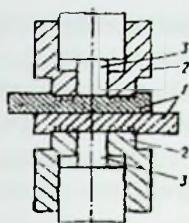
Схема сварки с предварительным зажатием свариваемых деталей.
